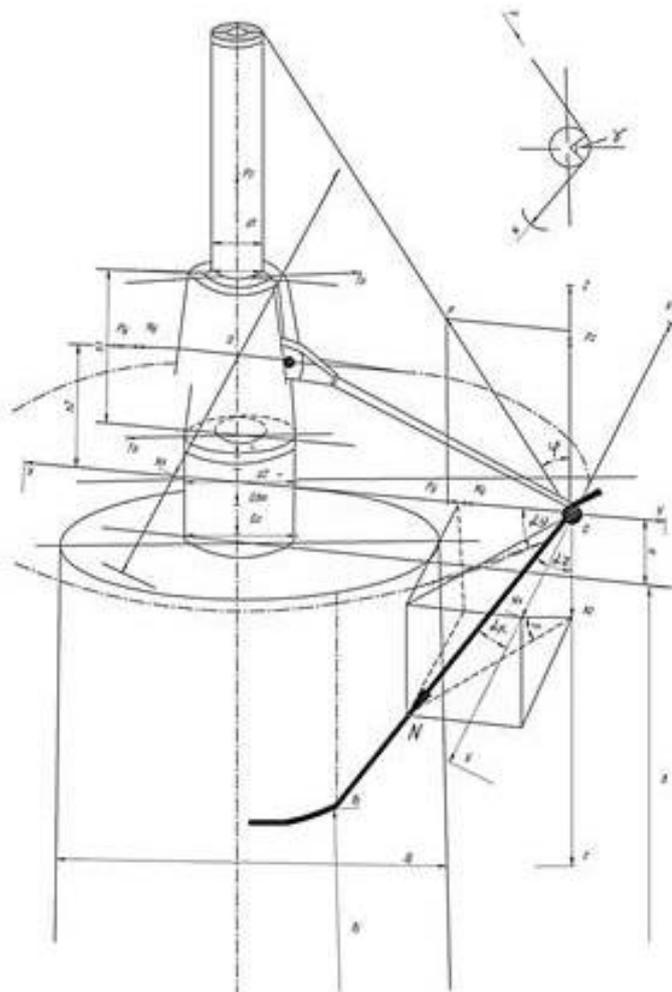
Схема нагрузки на приспособлении для разматывания нити в верхней части веретена
